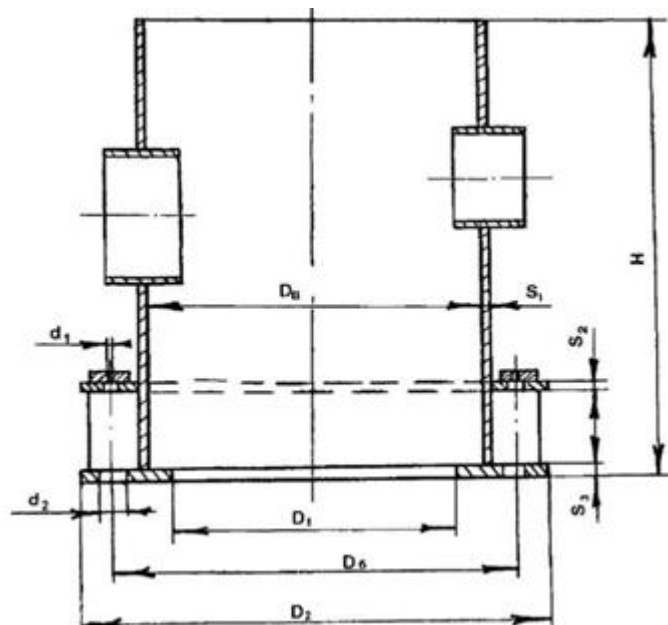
Розрахункова схема циліндричної опори для колонного апарата
